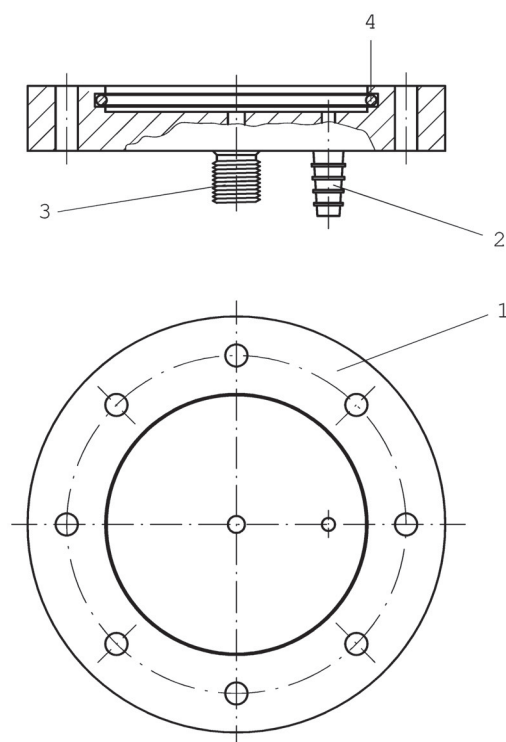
a: Flansch unten (1) inklusive Schlauchanschluss (2), Gewindestück (3) und O-Ring-Dichtung (4)
